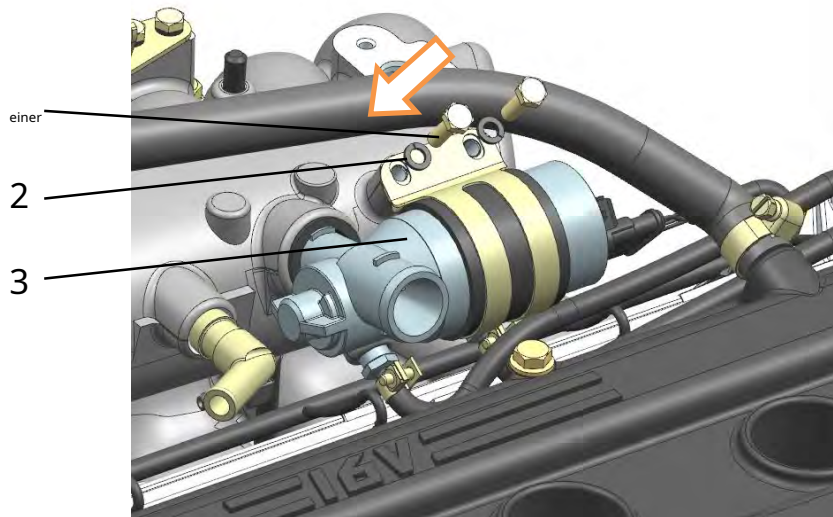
Einbau des O-Rings des Leerlaufreglerrohrs:
